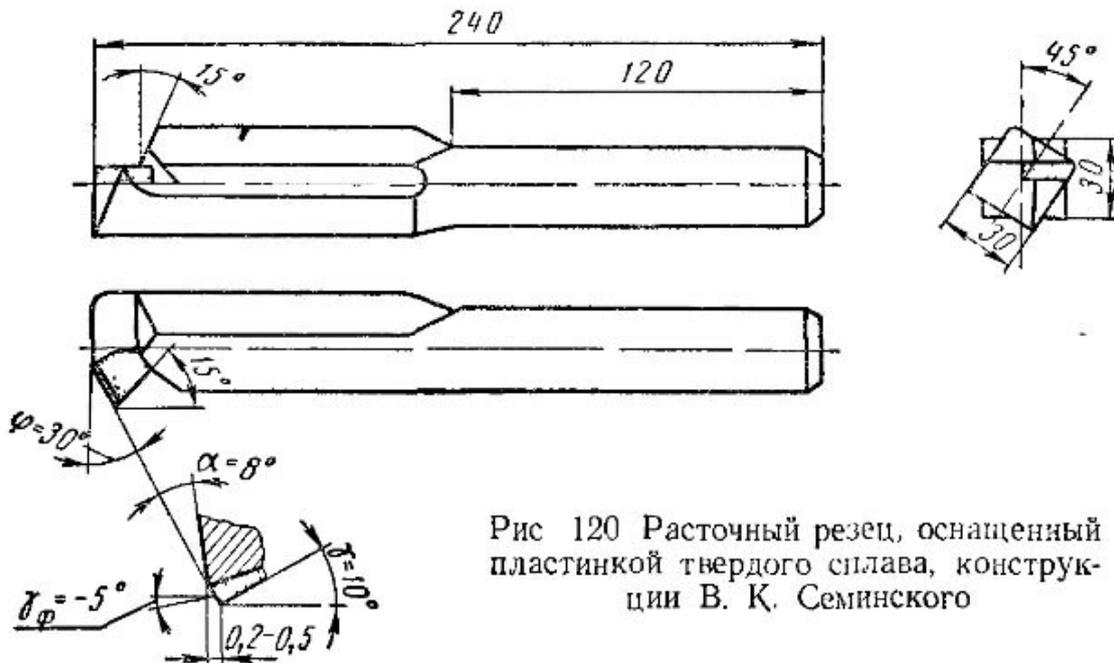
Расточный резец, оснащенный пластинкой твердого сплава, конструкции В. К. Семинского
